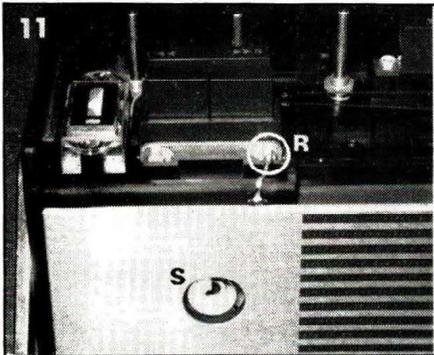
dessouder la connexion de masse de la cosse R. La laisser soudée du côté du panneau avant.
